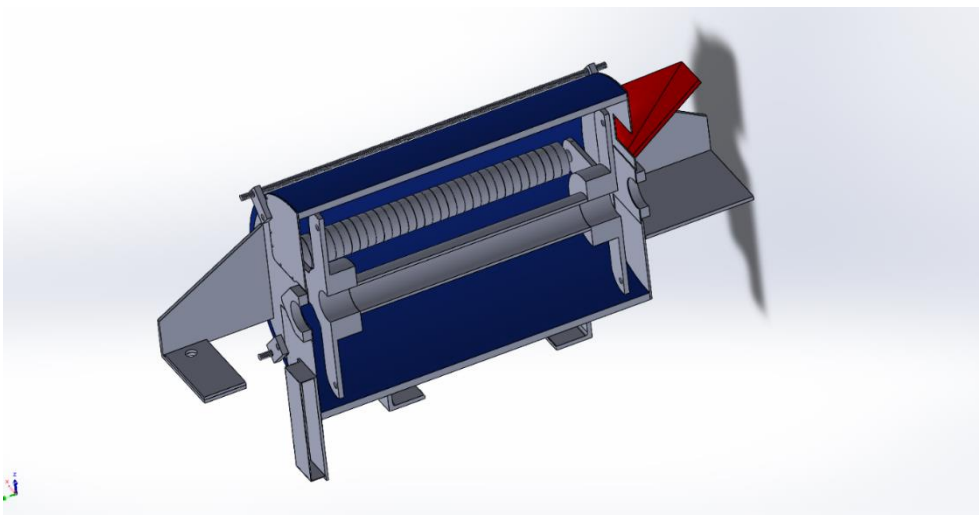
Exploded-View του συνολικού Assembly με τον μύλο, τον κινητήρα και τη βάση
